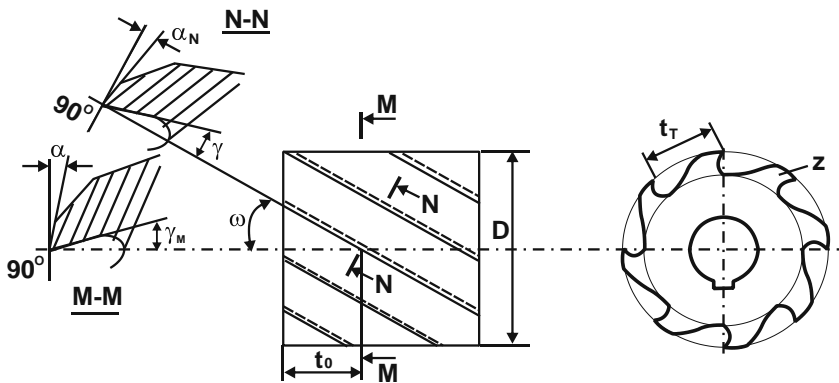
Загальний вигляд осьової циліндричної фрези та її конструктивних елементів
